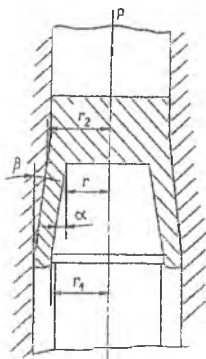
Схема выдавливания, совмещенного с раздачей трубной части заготовки
